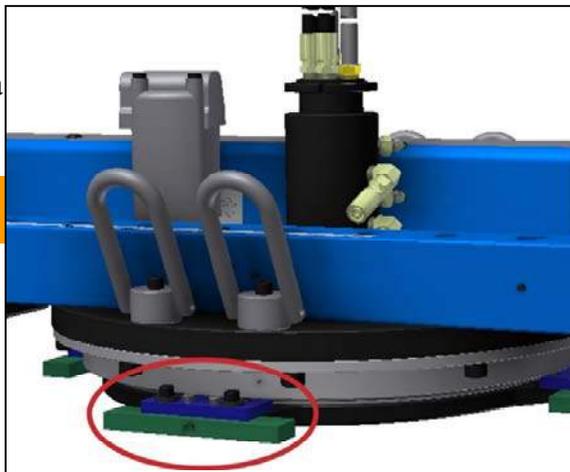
CONFIGURACION DEL KIT DE MONTAJE DE SUPERFICIE
